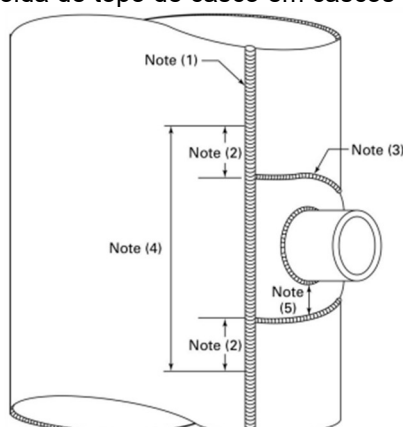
Placa de inserção nivelada (com ou sem bico/bueiro) com sua solda de topo cruzando a solda de topo existente em cascos ou cabeças
